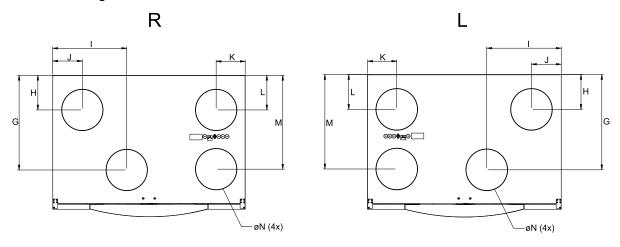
Dimensions vue de dessus, pour des unités en version droite (R) et gauche (L).
